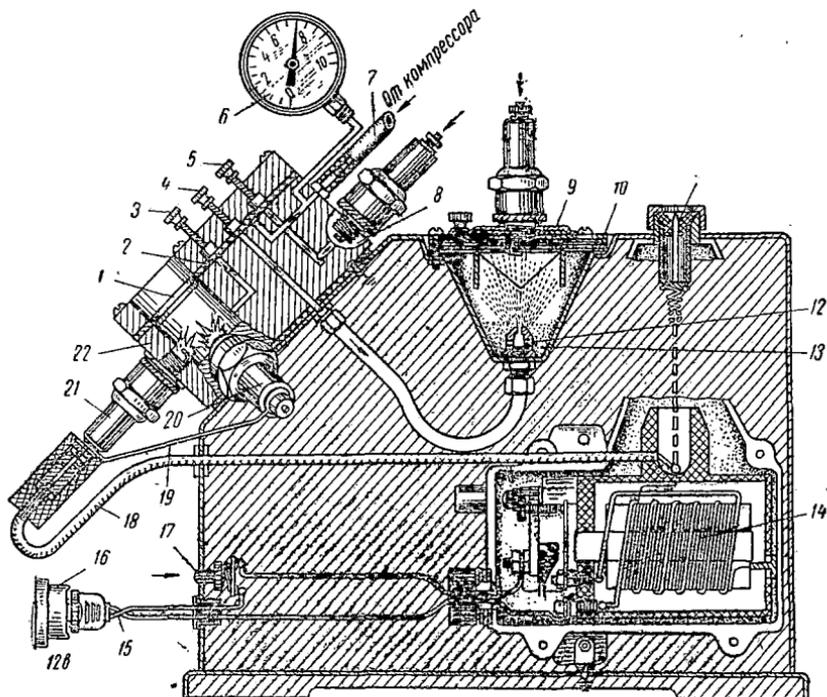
Схема прибора модели 514-2М для очистки и проверки свечей зажигания:
